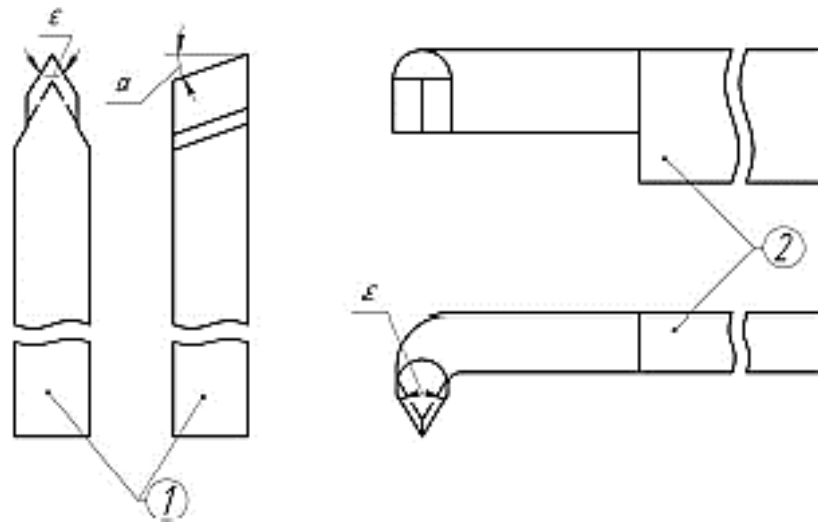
Види різьбових різців: (1 – для зовнішньої різьби, 2 – для внутрішньої різьби)
